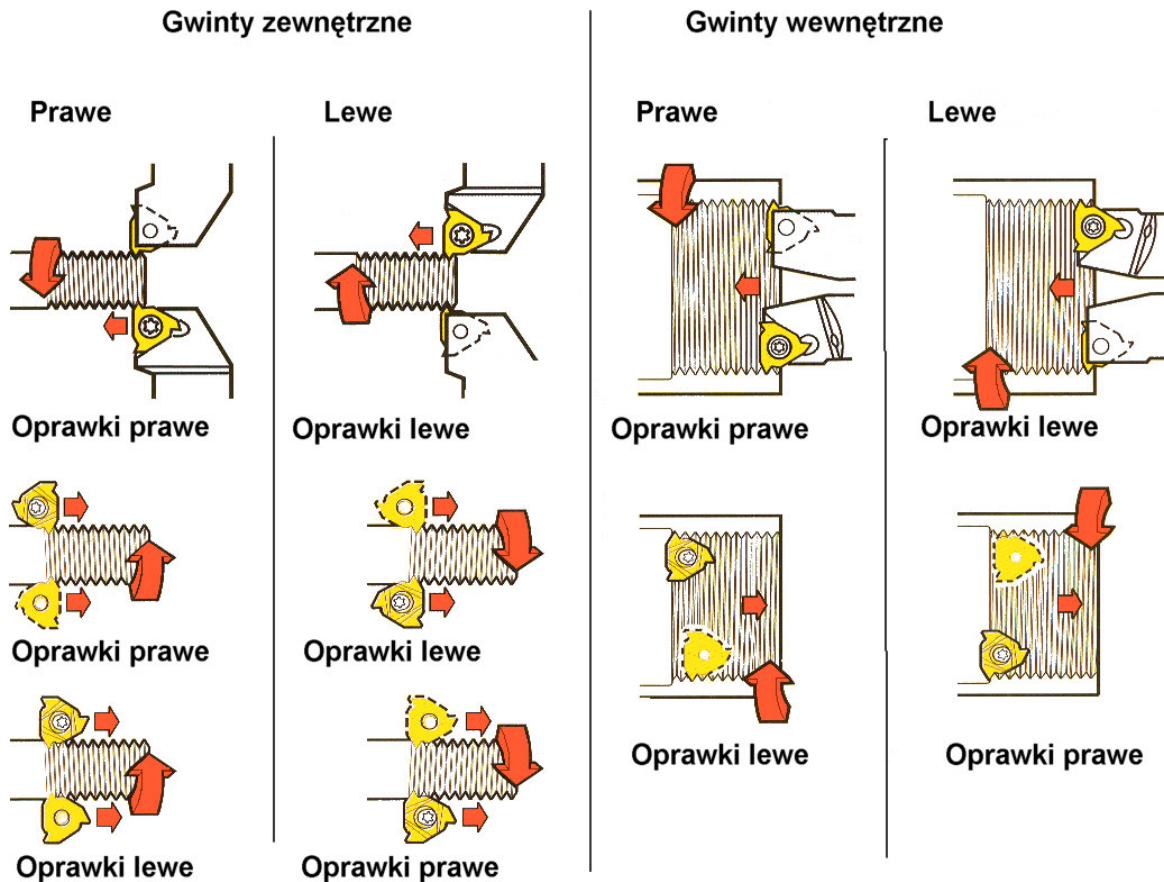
Kierunek wcinania przy bocznym podziale nadatku obróbkowego [Sandvik Coromant]
